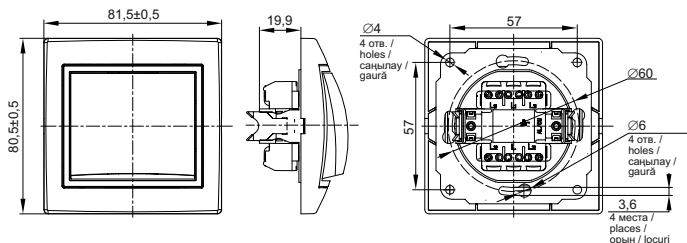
Габаритные и установочные размеры выключателя со степенью защиты IP44 /
